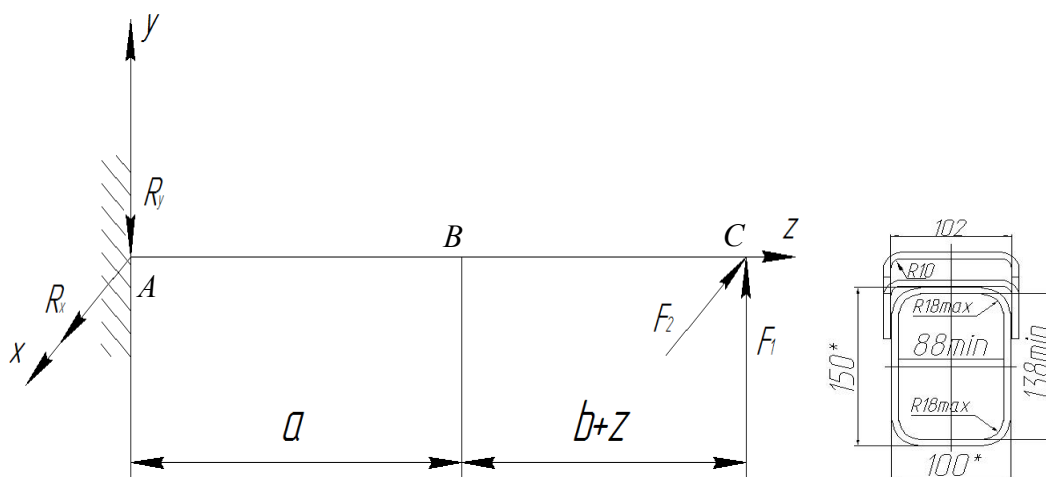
Расчетная схема балки и поперечное сечение на участке a
